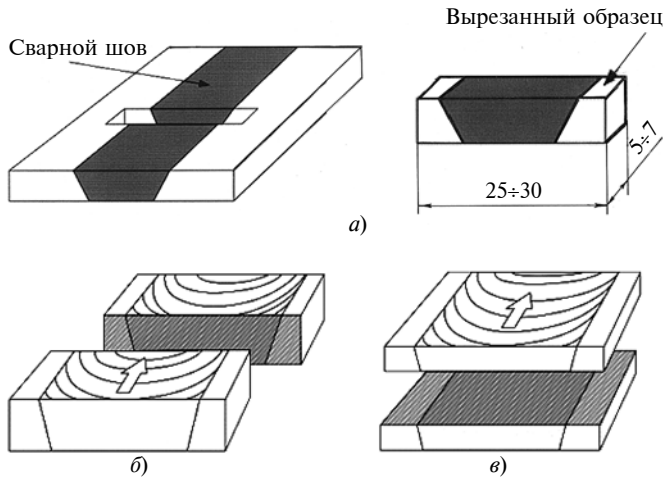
Схемы (а–в) вырезки образцов для металлографических исследований поперечного сечения сварного соединения
